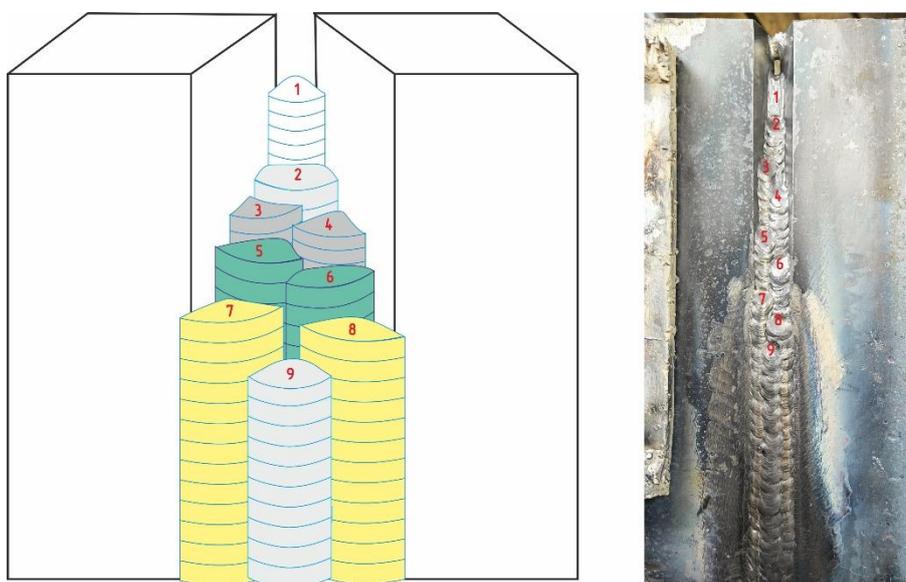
Многослойная сварка стыкового соединения в вертикальном положении
